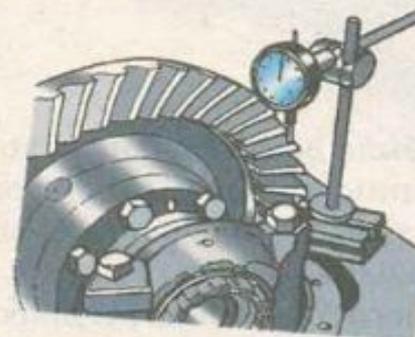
Проверка бокового зазора в зацеплении зубьев шестерен главной передачи (мост с балкой типа банджо)
